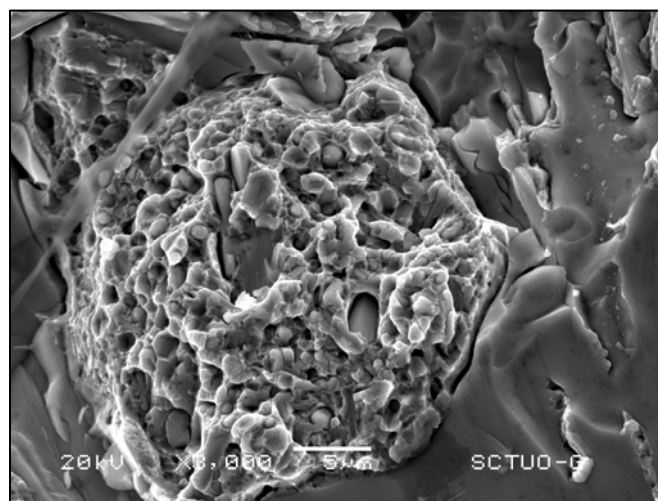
Dendrito rodeado de carburos en la superficie fracturada de la fundición con alto contenido en cromo (3.000x)
